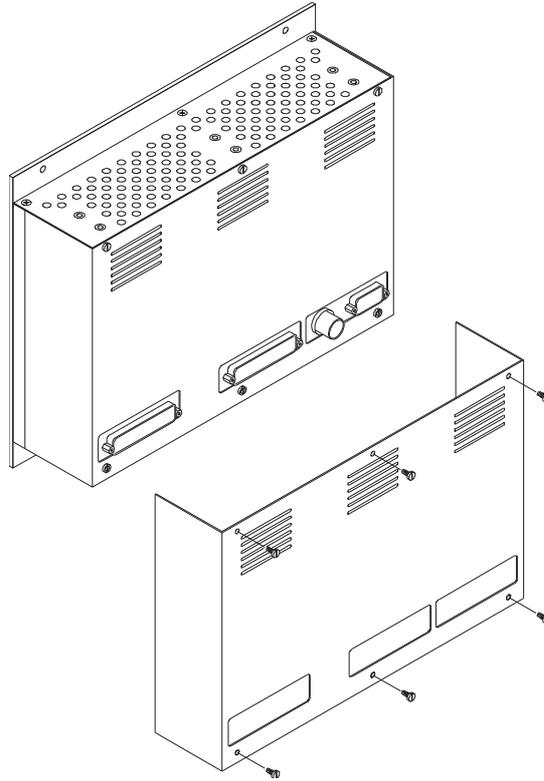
Befestigen des hinteren Abdeckbleches
